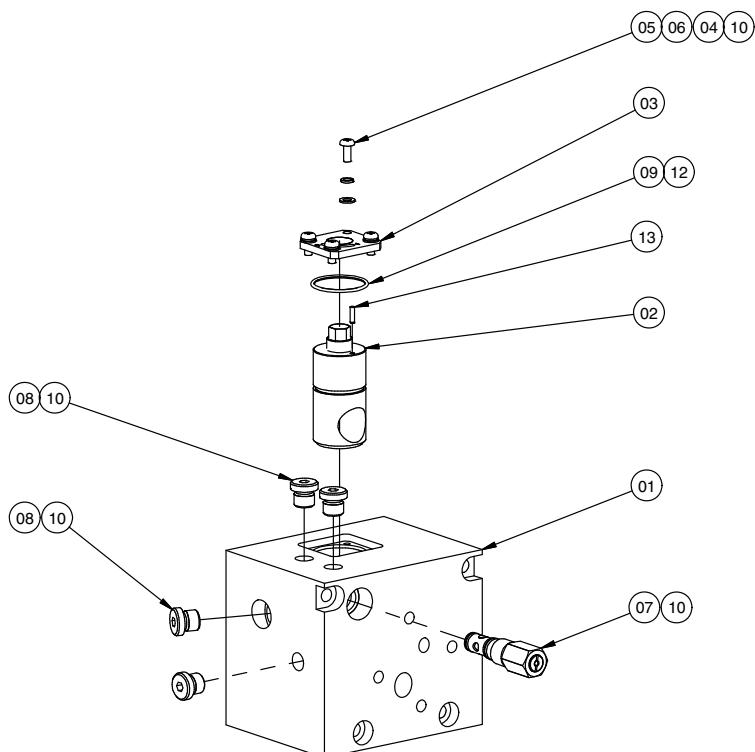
Peças para adaptador de bomba de caudal simples
